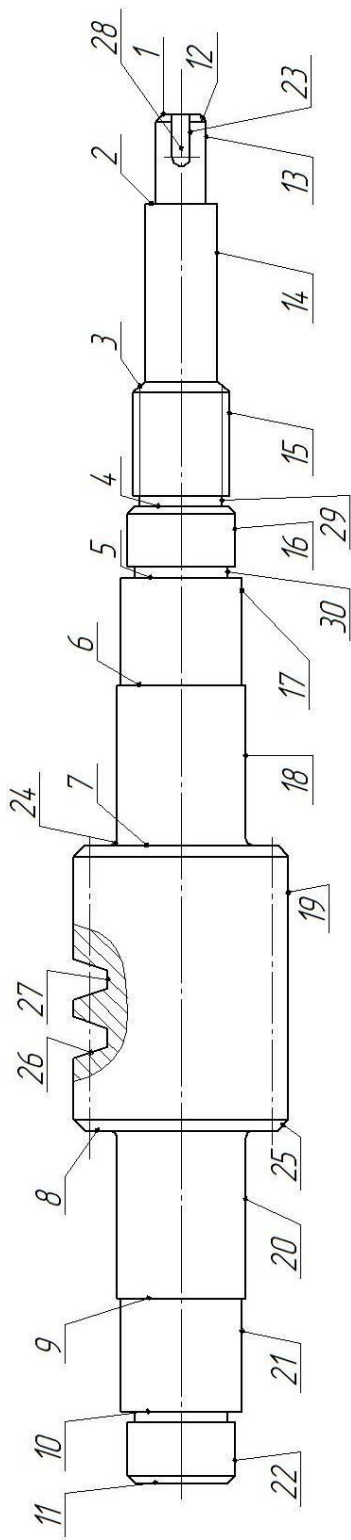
Эскиз с нумерацией поверхностей
